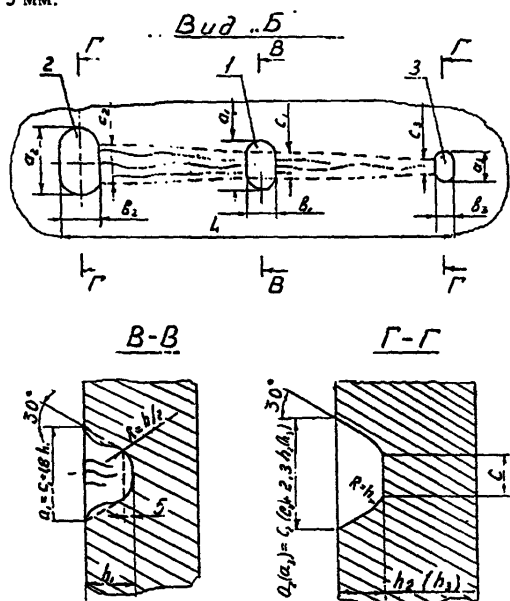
Схема расположения и профиль полостей-ловушек при восстановлении живучести литых корпусов путем выборки зоны до неповрежденного металла в трещиноватой зоне малой глубины.
